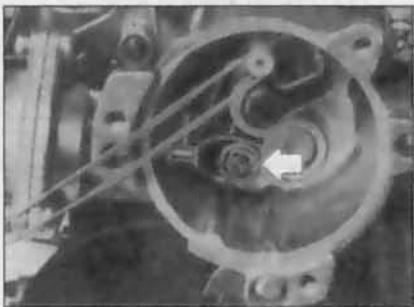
Регулировка зазора воздушной заслонки карбюратора Keihin (Глава 11)
